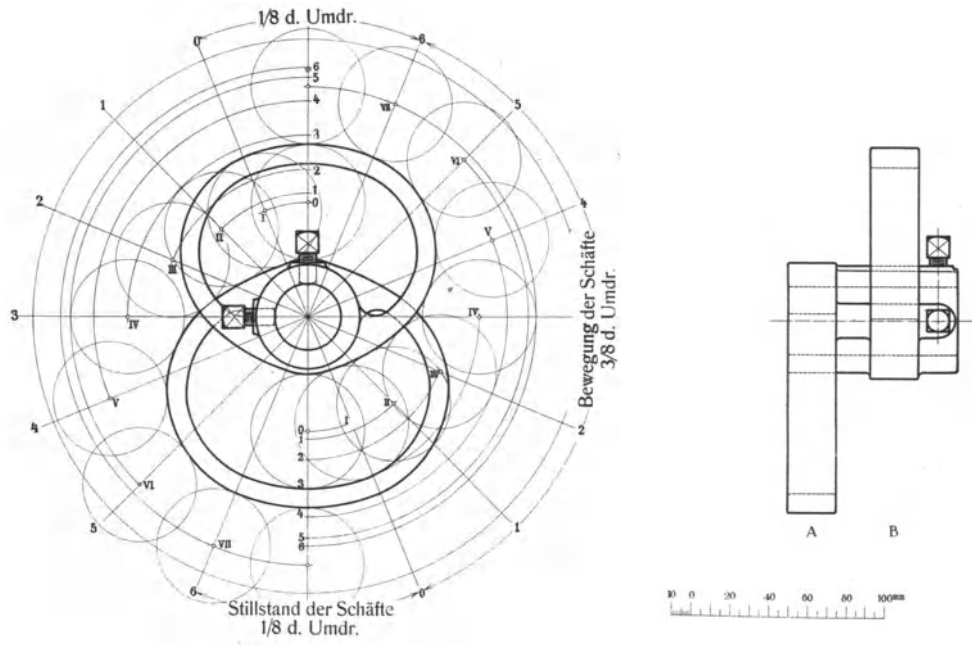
35. Konstruktion des Leinwandexzentrers (Schaftstillstand, 1/8 Umdrehung der unteren Welle, ungleichmäßige Schafsbewegung).
